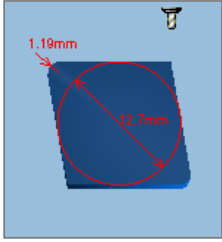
Пластинка різця «SCMT 12 04 12-PR 4425»
